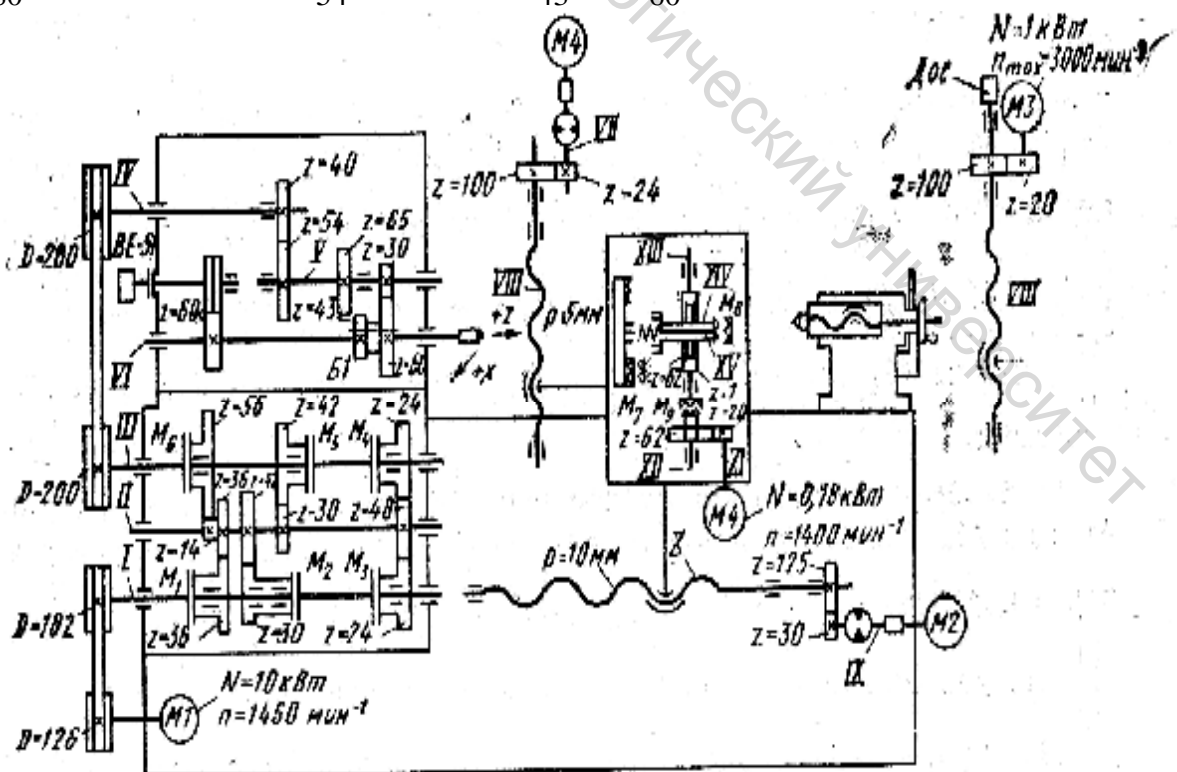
Кинематическая схема станка мод. 16К20ФЗ
